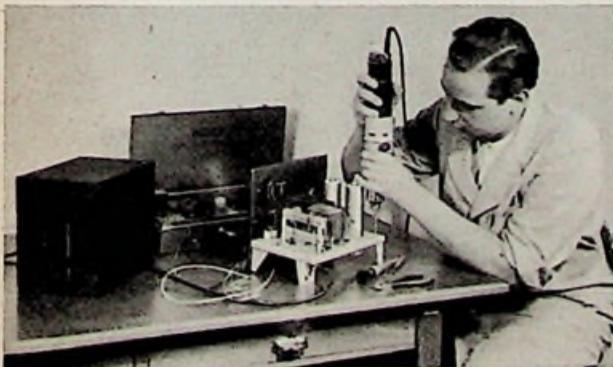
Verwendung des Bosch-Combi-Elektrowerkzeuges als Handbohrmaschine
